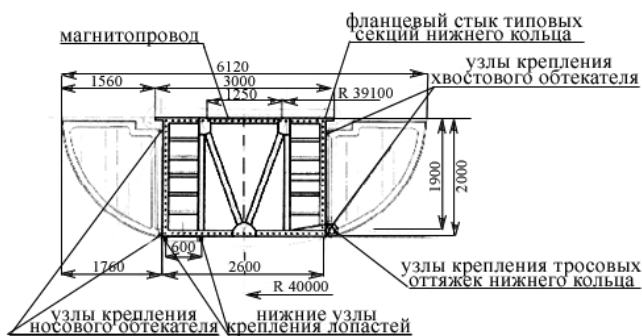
Фрагменты конструкции нижнего кольцевого ротора
